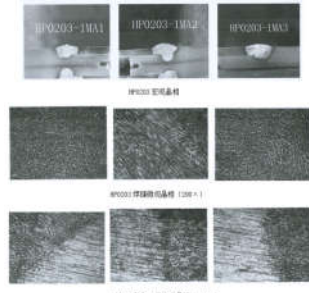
焊缝3 (试件 HP0203) 晶相样貌
